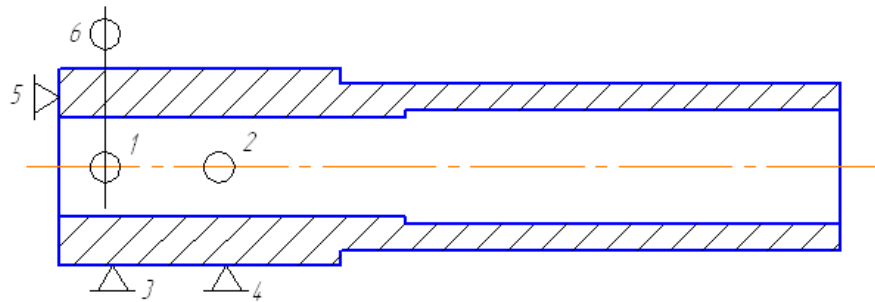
Схема базування та закріплення заготовки на операції механічної обробки – 005. Токарна з ЧПУ
